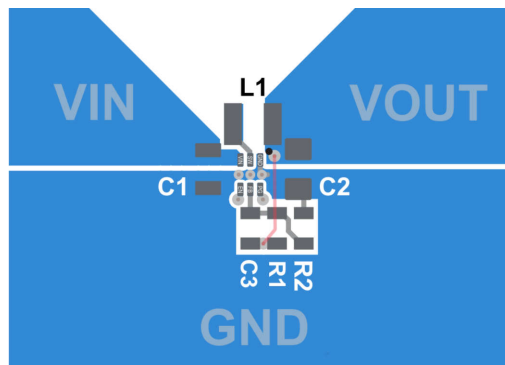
TPS62A0x (SOT563) PCB Layout Recommendation
